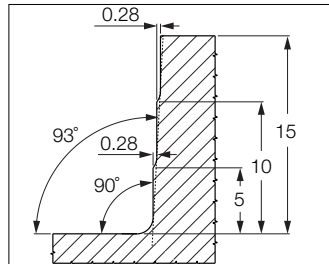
Профиль за несколько проходов при ступенчатом фрезеровании (глубина 15 мм)
